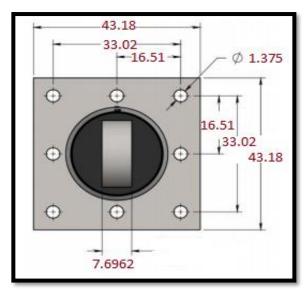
Dimensiones de la placa base para el disipador de 330 kip. Fuente: Propia.
